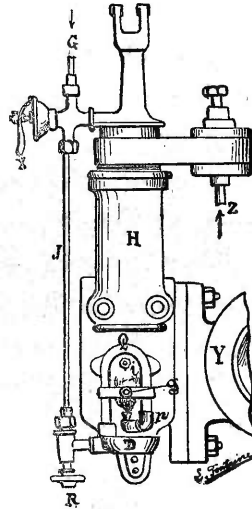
Vue d'ensemble du vaporisateur Niel.
